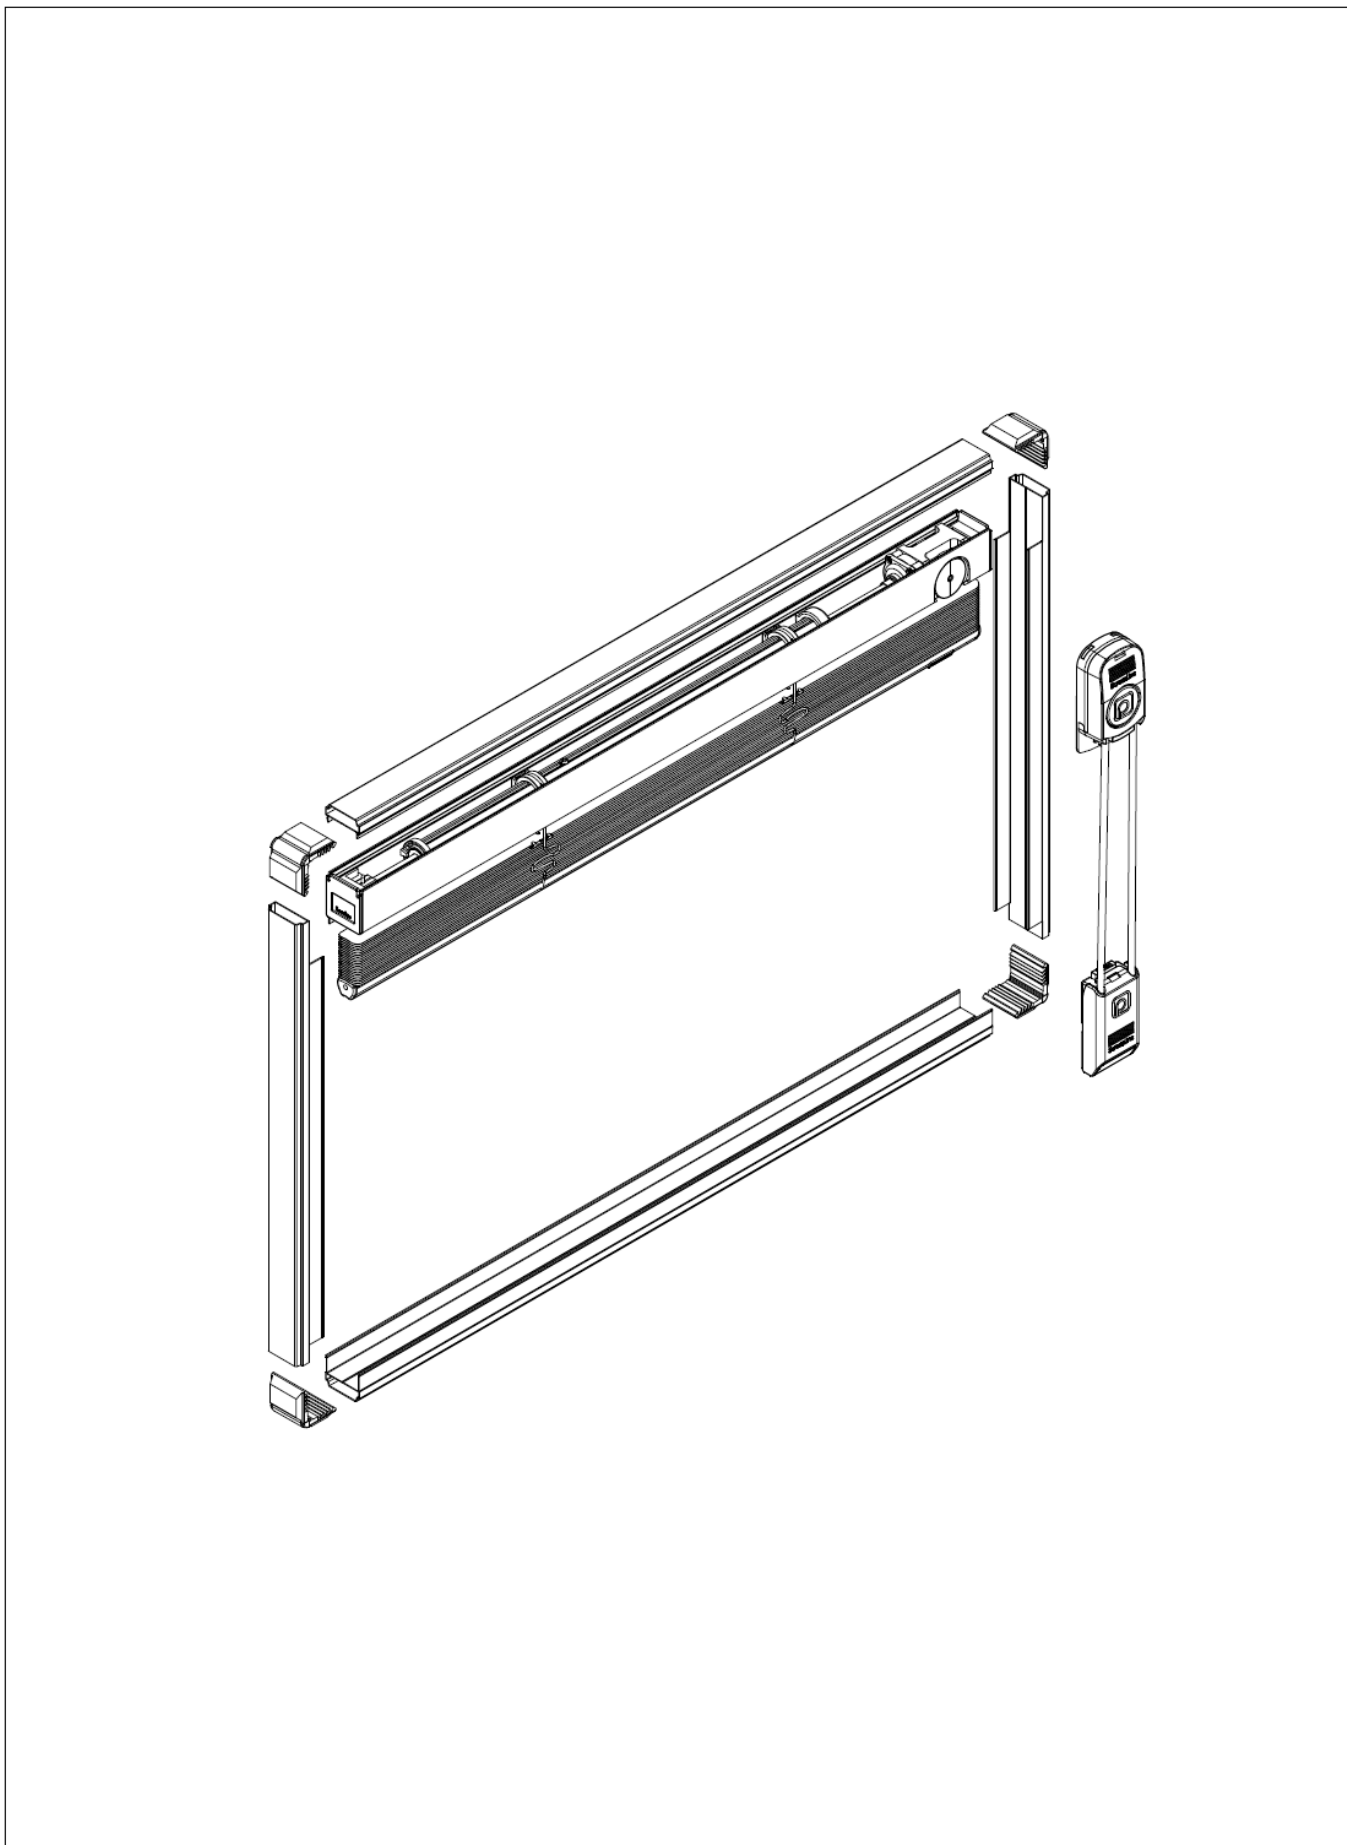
Vue d'ensemble éclatée - Store en position relevée
